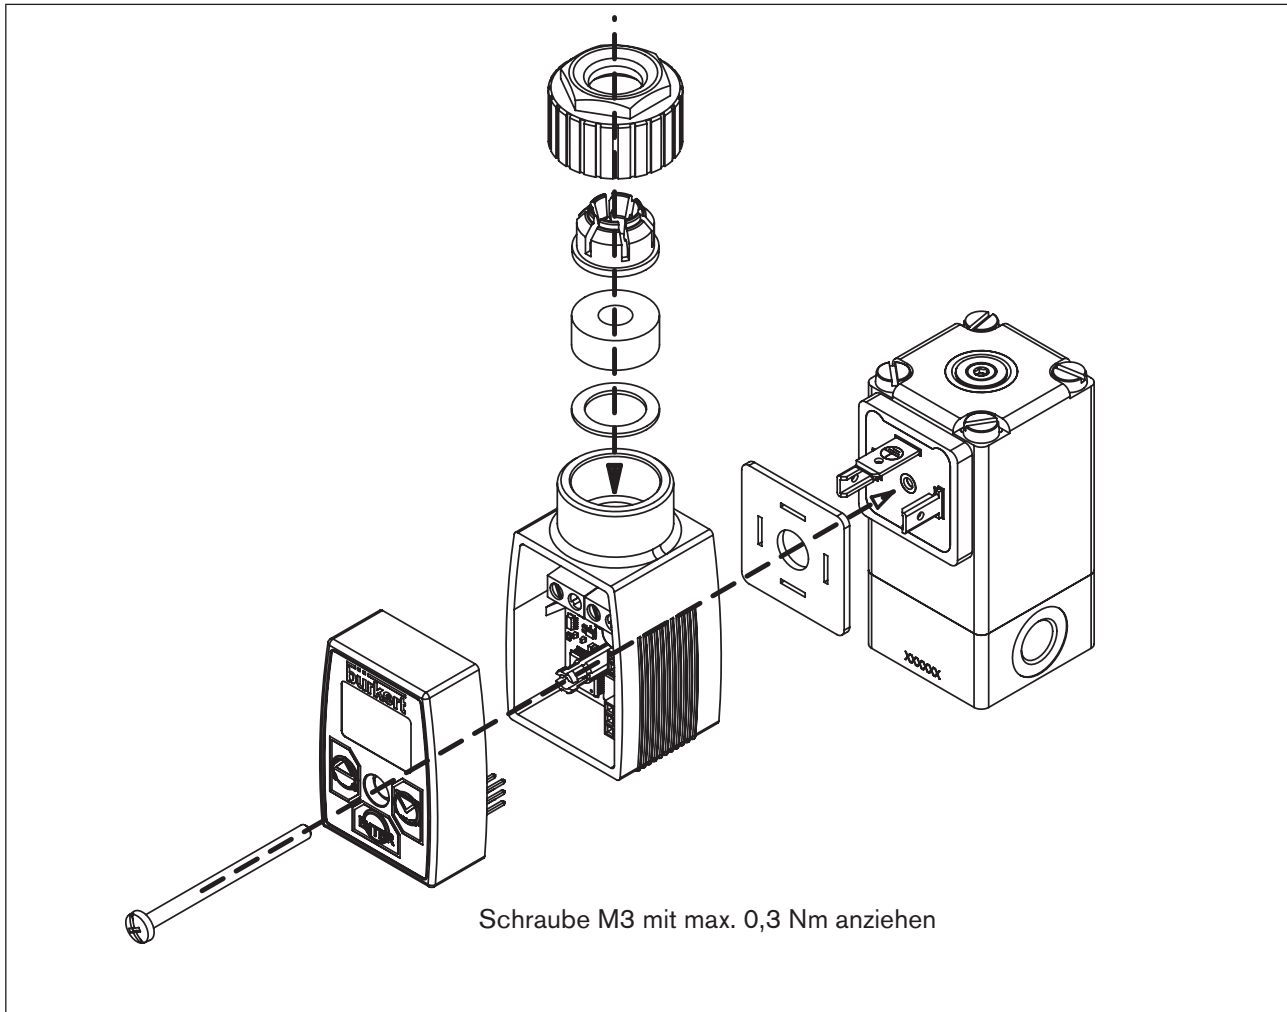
Montage der Gerätesteckdoseausführung an das Ventil
